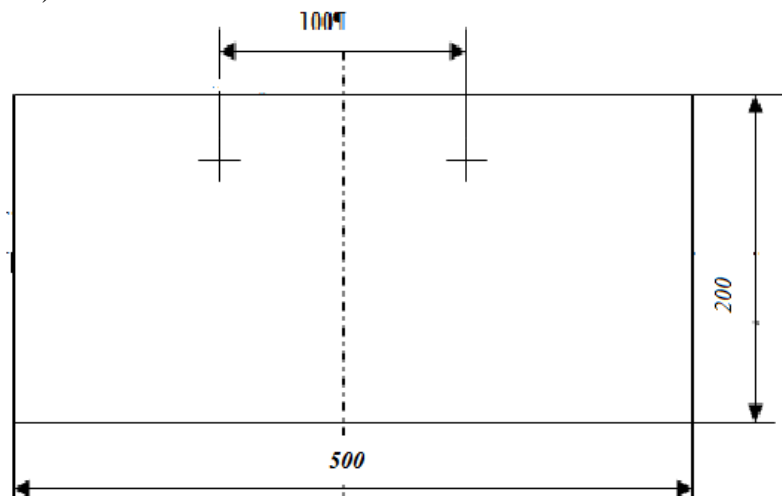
Разметка пластины до наплавки валика на кромку
